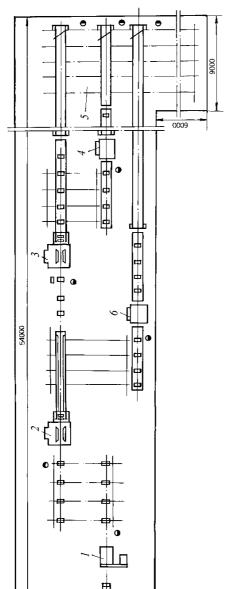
Схема лесопильного цеха для агрегатной переработки сырья: I – окорочный станок; 2 – ЛАПБ; 3 – торцовочное устройство для досок; 4 – конвейер; 5 – сортировочное устройство для досок
